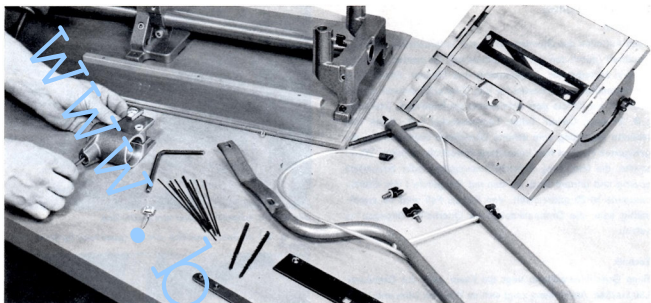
Am Sticksägegehäuse wird die Klemmschraube gelöst.
